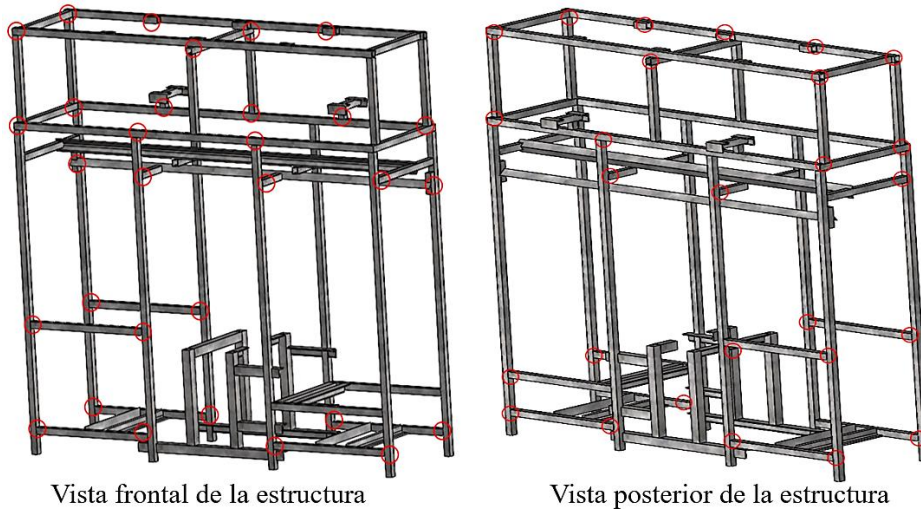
Sección de soldadura para tubo cuadrado.
